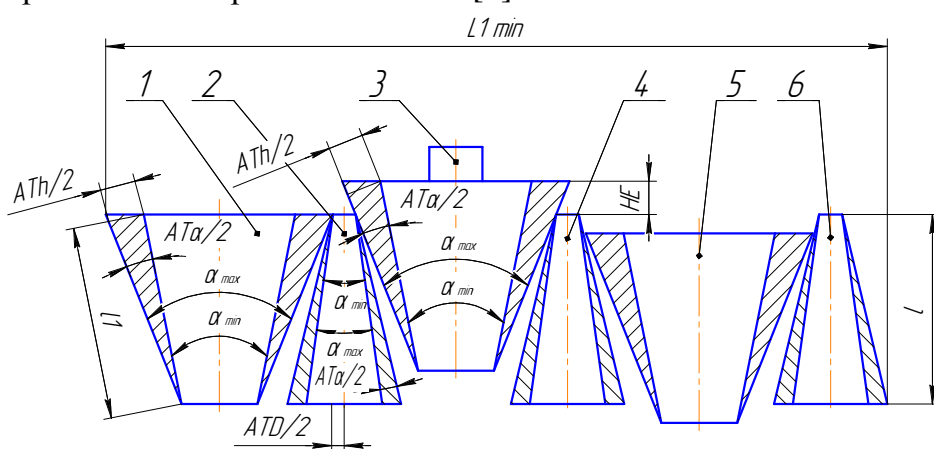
Схема полей допусков при сборке «однослойного» бесепараторного подшипника с расположенным между цилиндрическими роликами 1, 2, 4, 5, 6 контракалибра 3 в верхнем его положении при минимальных отклонениях угла конуса [1, 2]
